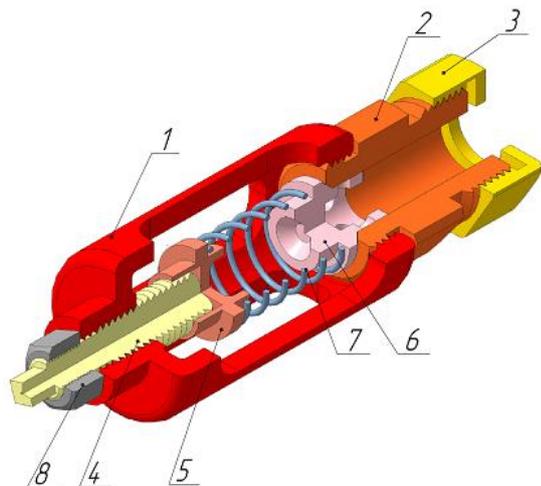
Трехмерная модель предохранительного клапана: 1 – корпус, 2 – седло, 3 – гайка, 4 – винт, 5 – опора, 6 – клапан, 7 – пружина, 8 – гайка
